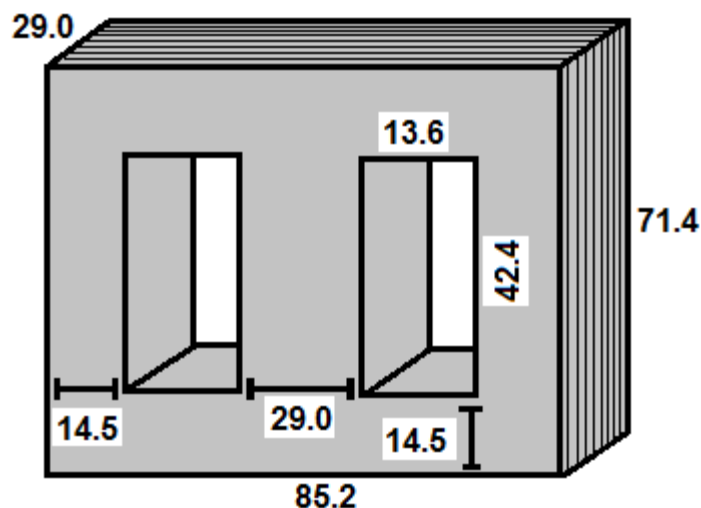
Núcleo do transformador. Dimensões geométricas em milímetro
